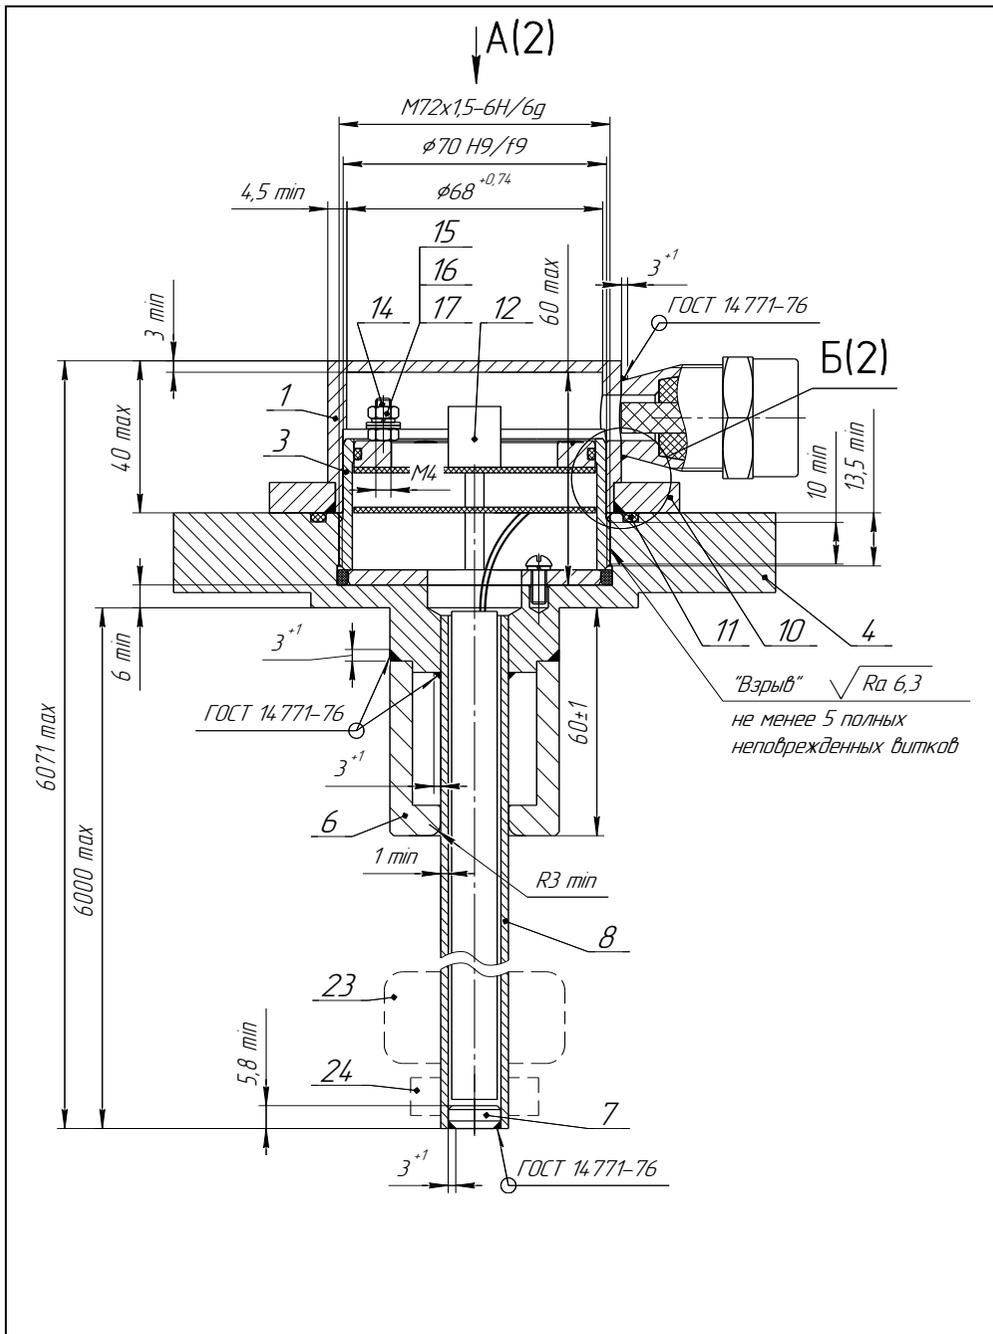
(лист 1 из 4) – Чертеж средств взрывозащиты варианта со сварным корпусом из нержавеющей стали (НЖ)
